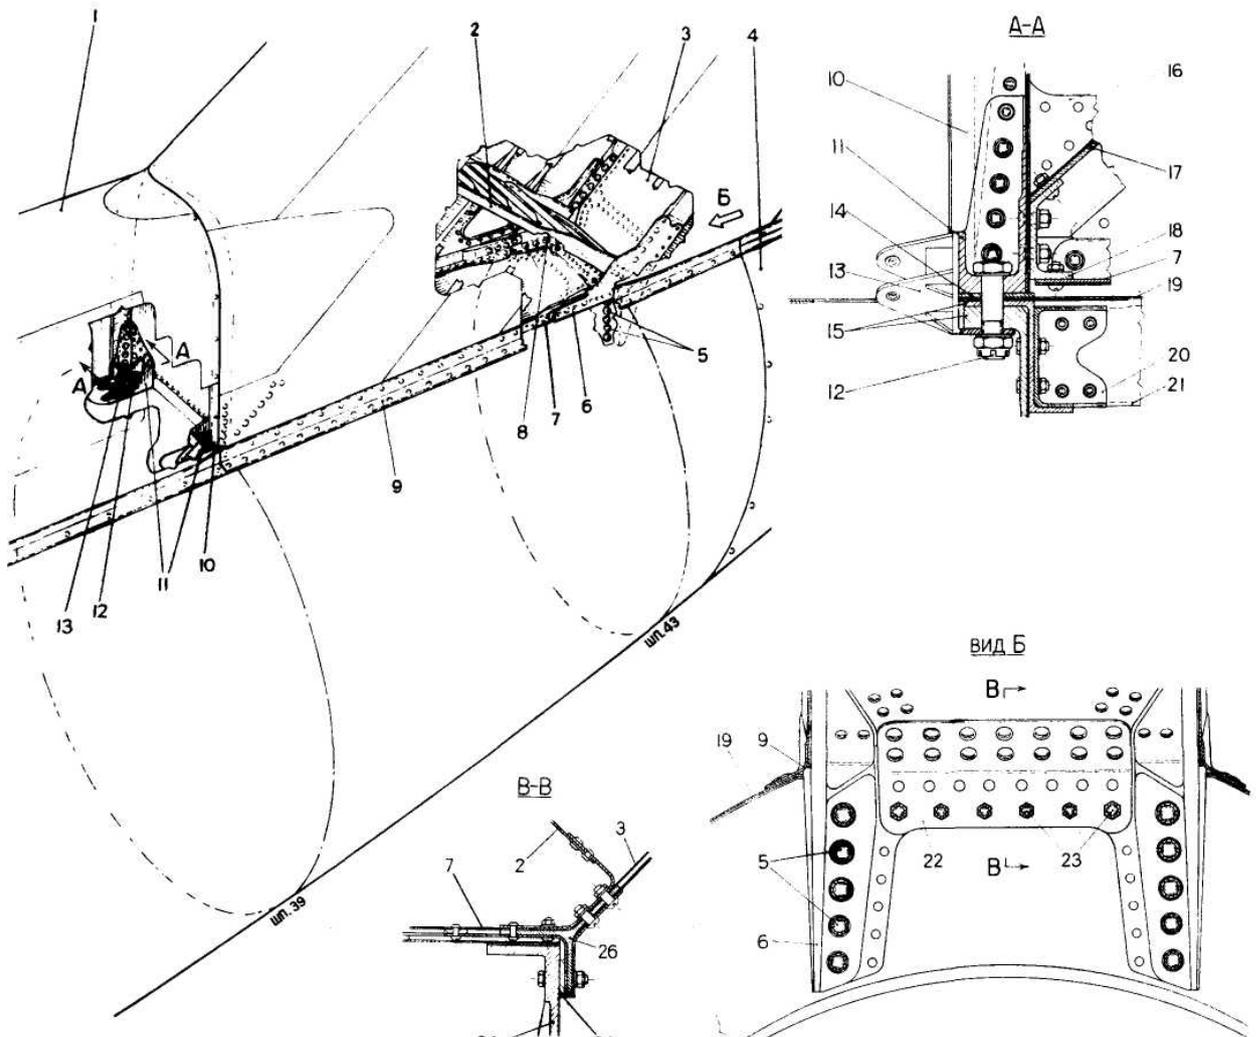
СТЫКОВКА КИЛЯ С ФЮЗЕЛЯЖЕМ
